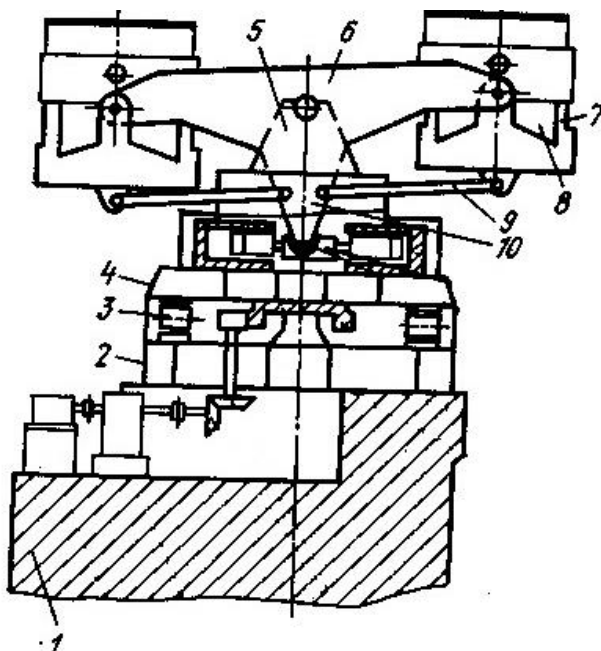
Сталеразливний стенд конструкції ВАТ «УЗТМ»
